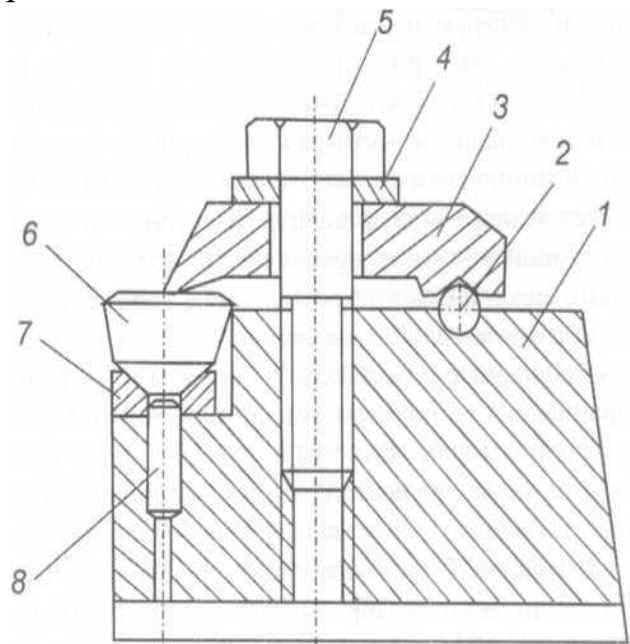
Конструкція різцевої державки: 1 – корпус, 2 – опорна кулька, 3 – притискна планка, 4 – шайба, 5 – гвинт, 6 – різальна пластина, 7 – сепаратор, 8 – штифт.
